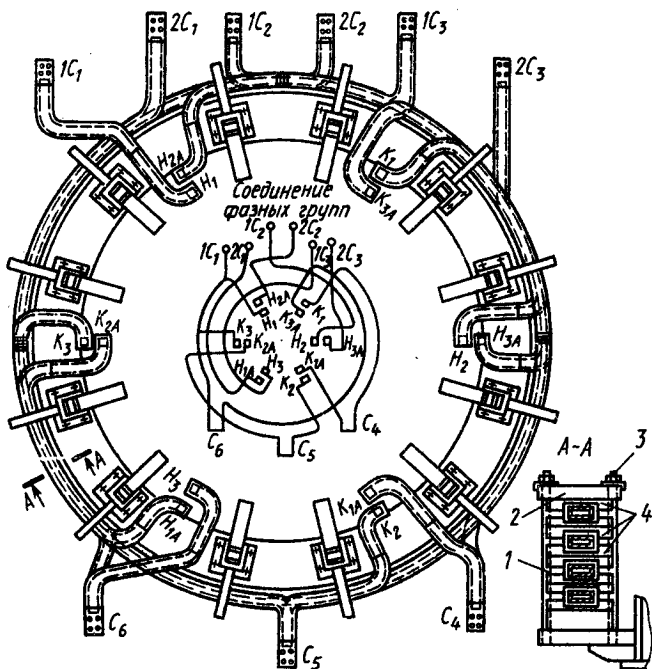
Расположение соединительных шин обмотки статора турбогенератора ТВВ-320-2:
